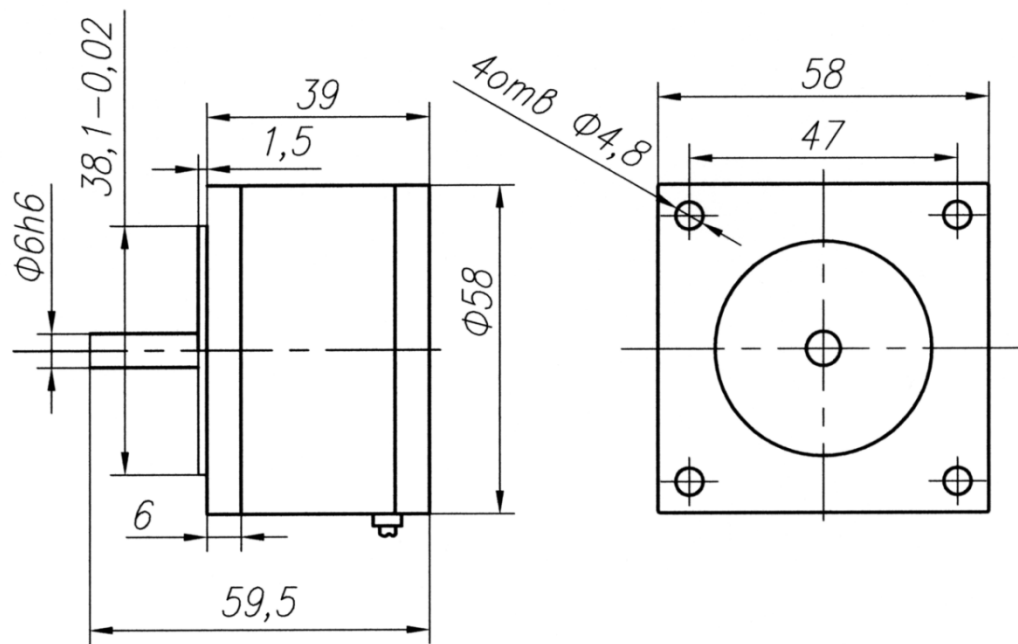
Габаритные и посадочные размеры шагового электродвигателя ДШИ-200-1-1
